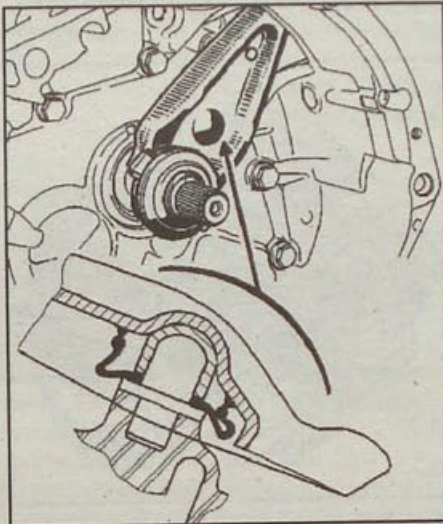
Расположение чехла для опоры вилки выключения сцепления, заполненного смазкой (коробка передач JC)
